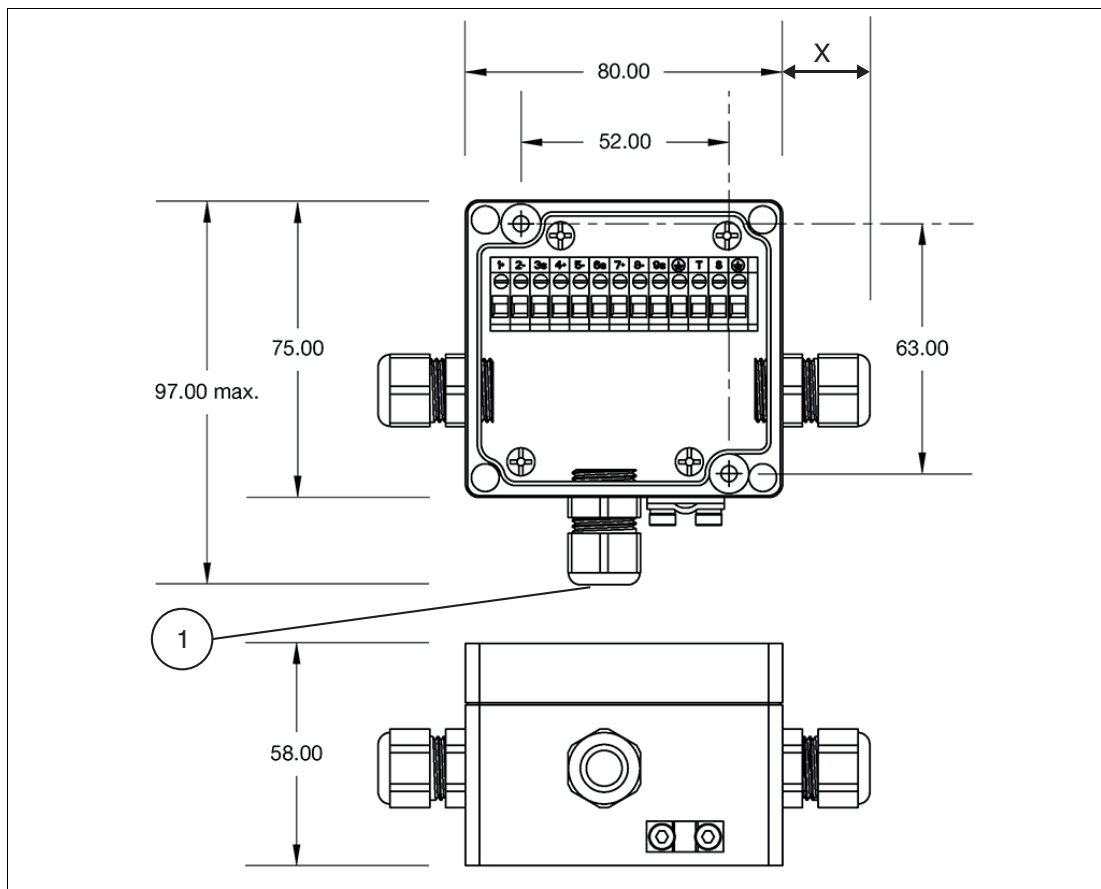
Mechanische Abmessung des F4-Gehäuses
